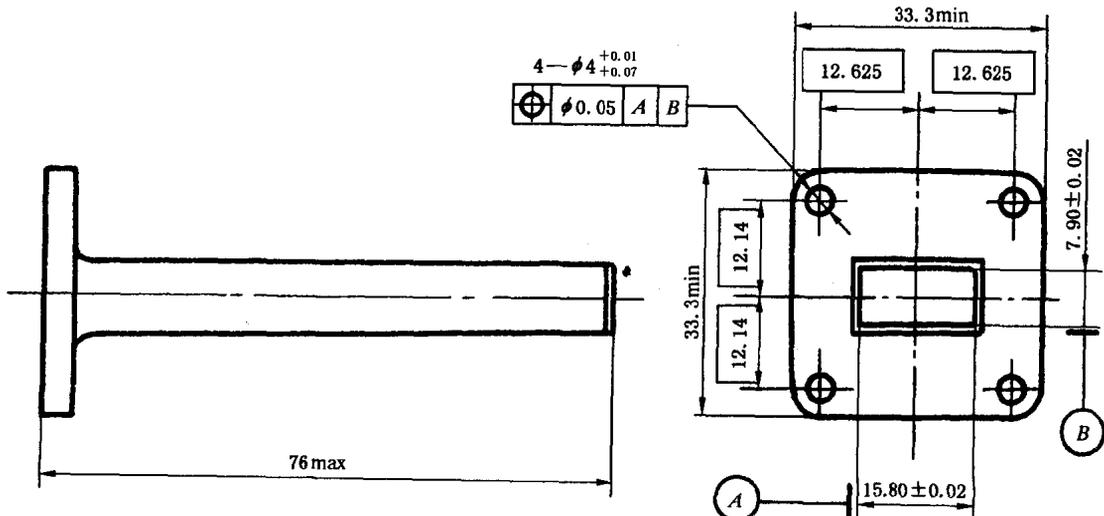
GH 12514A 波导负载的结构型式、外形尺寸和连接尺寸
